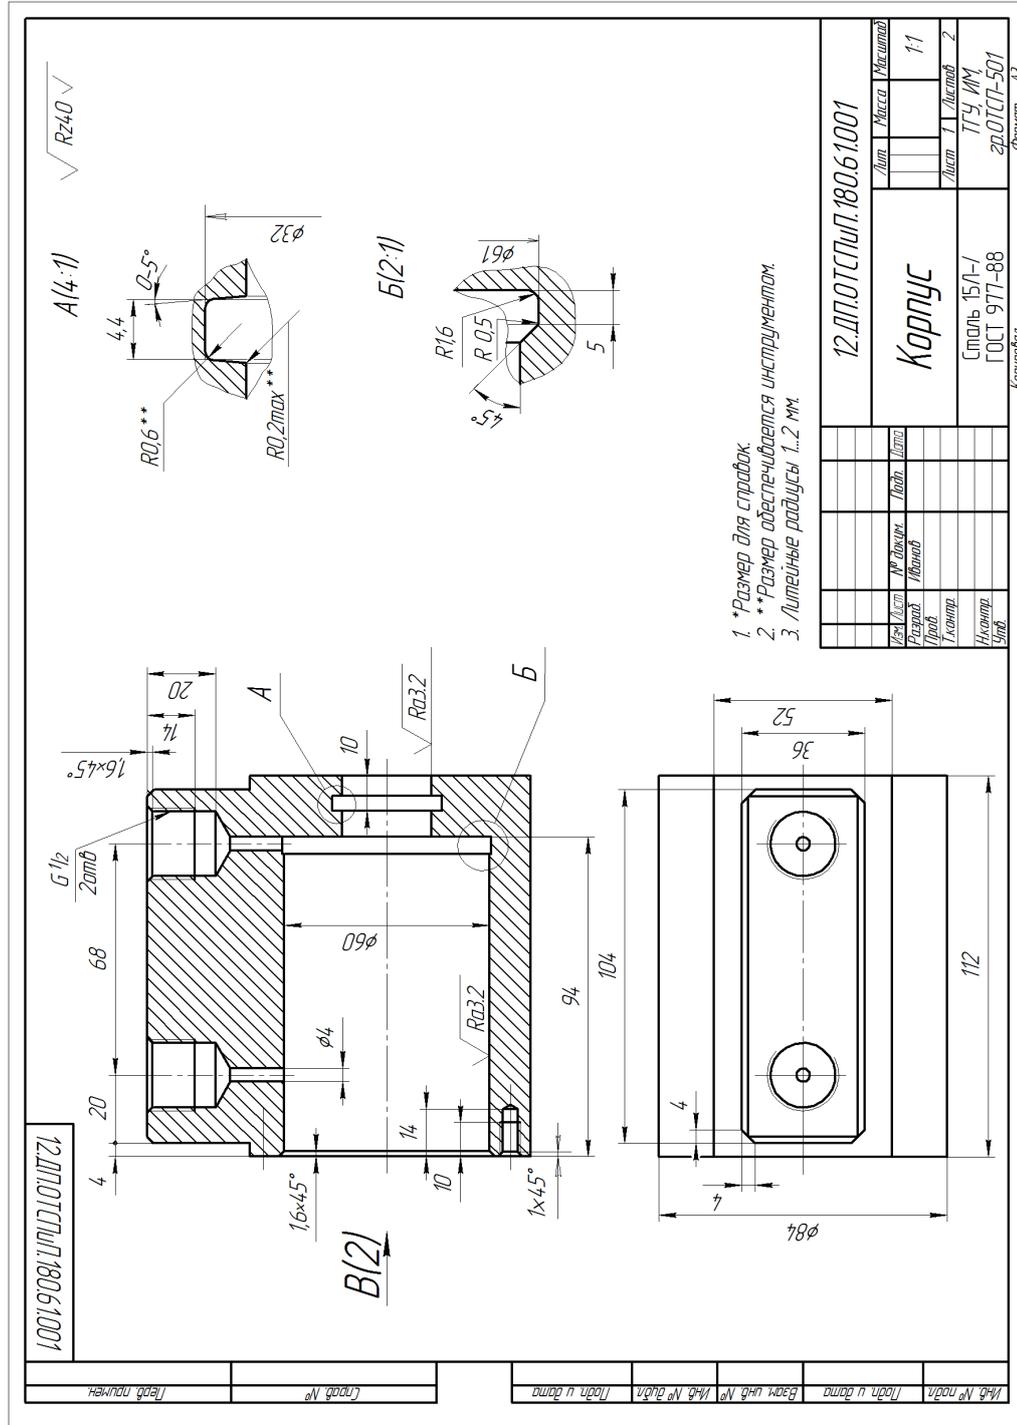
Чертеж корпусной детали (первый лист)
